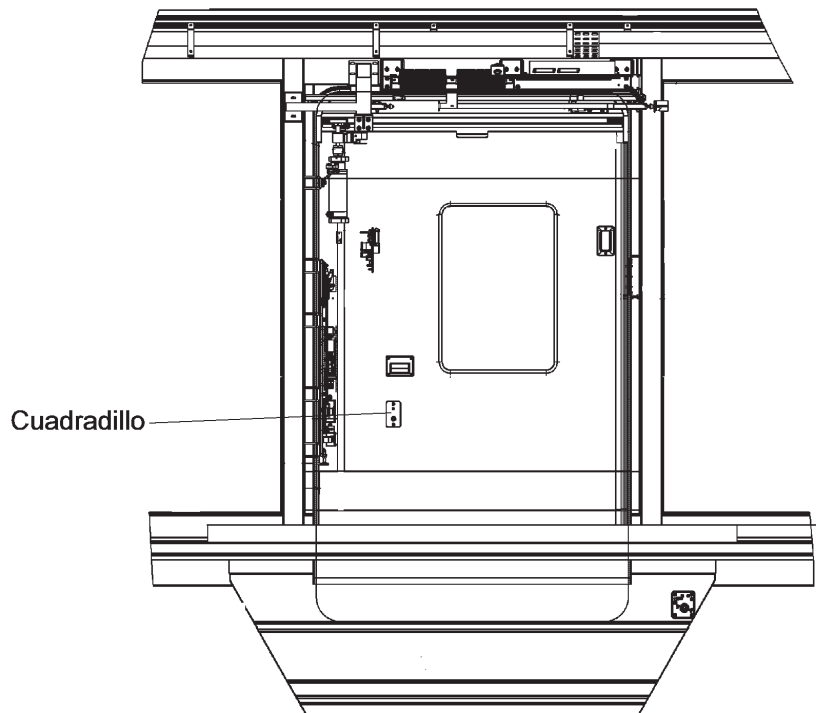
Condena de una puerta de acceso rampa - estribo
